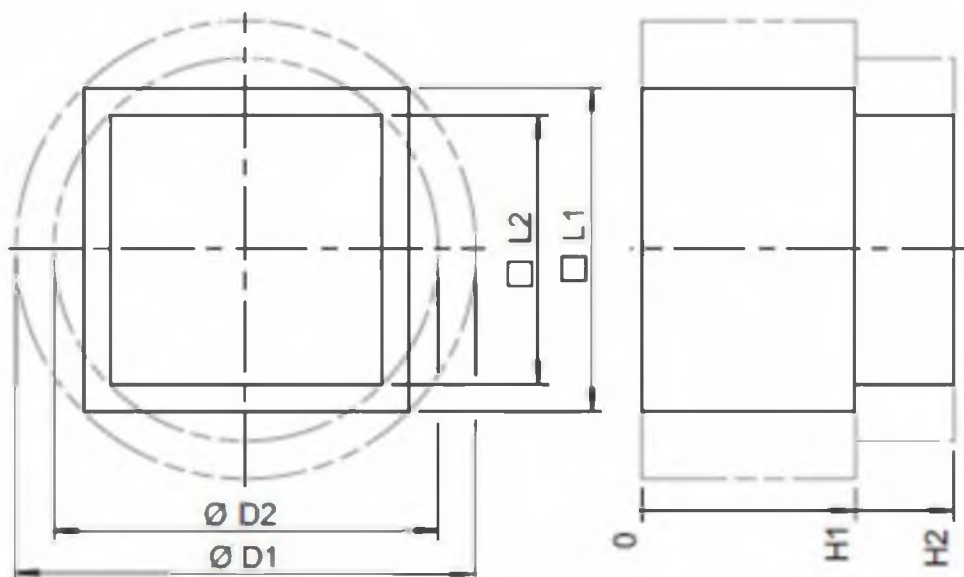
Габаритні розміри деталі при положенні столу 102°
